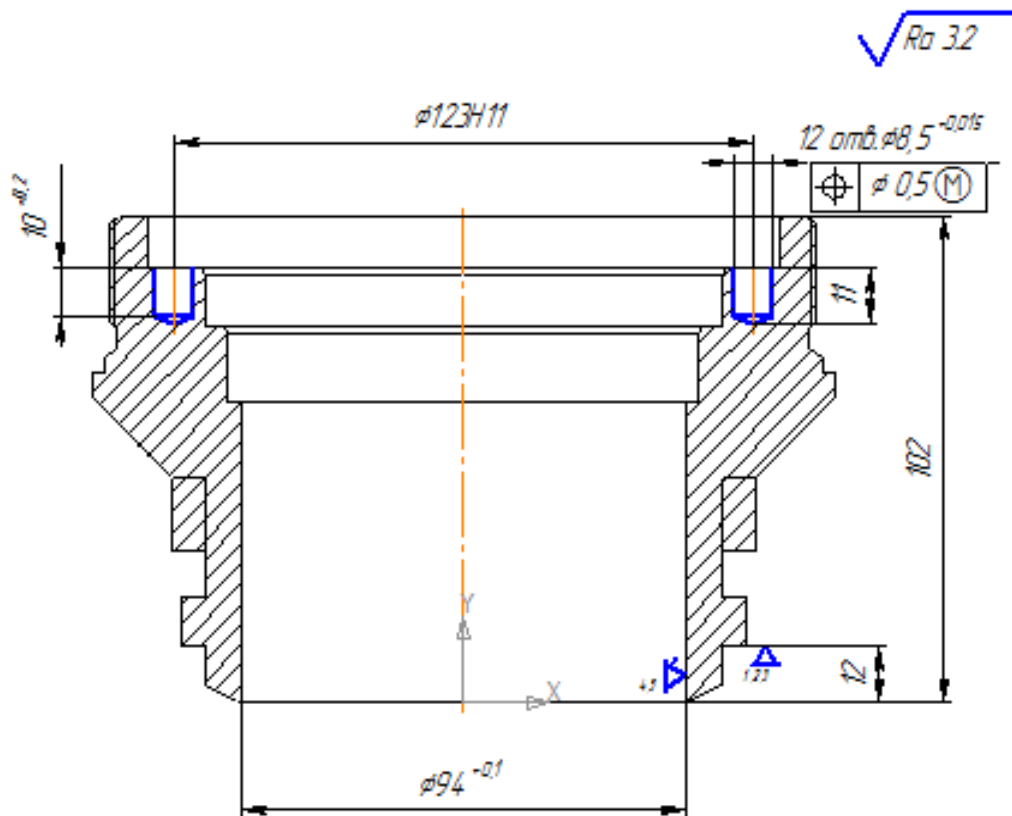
Схема базування заготовки на операції комплексній з ЧПК 025
